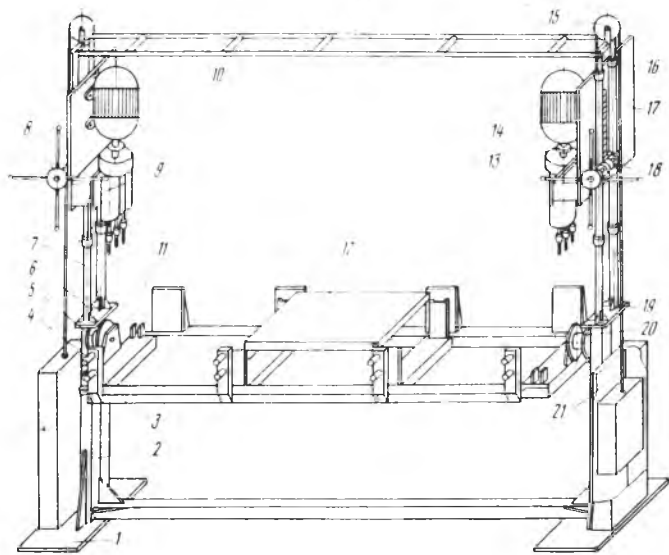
6-шпиндельный вертикально-сверлильный станок (вайма):
